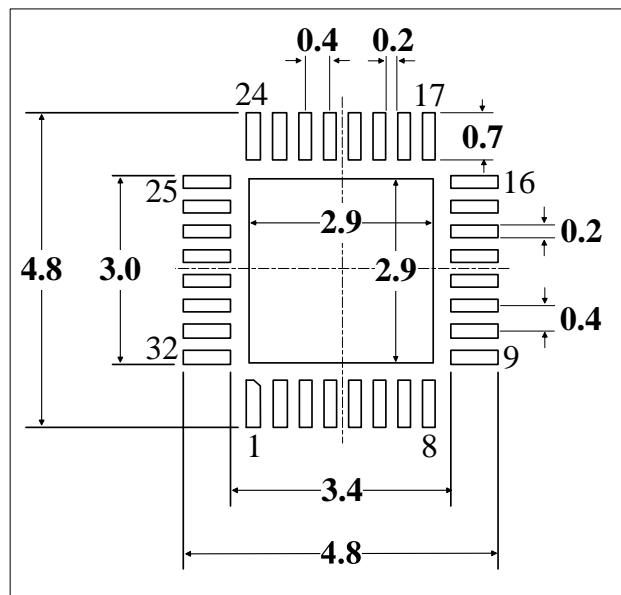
QFN32(4x4mm)封装焊盘建议⁽¹⁾
